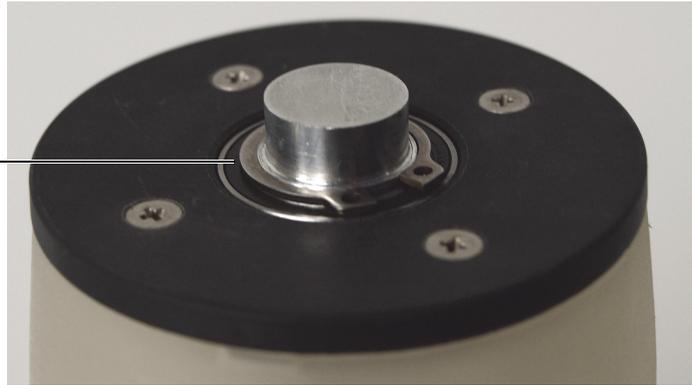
Herunterdrücken des C-Clips in die Rille am Sensorachsenende mit dem Hilfswerkzeug
